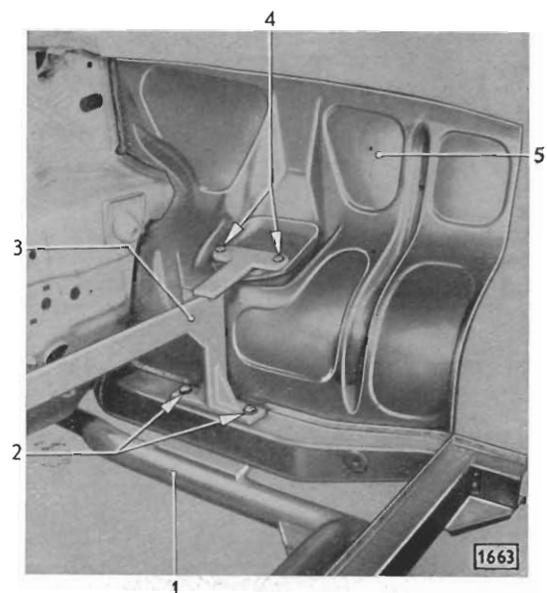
Linken Radeinbau an Längsträger und Stirnwand außen angelegt und an Radeinbau-Ausrichtlehre festgeschraubt – rechten Radeinbau in gleicher Weise in Einbaulage bringen
